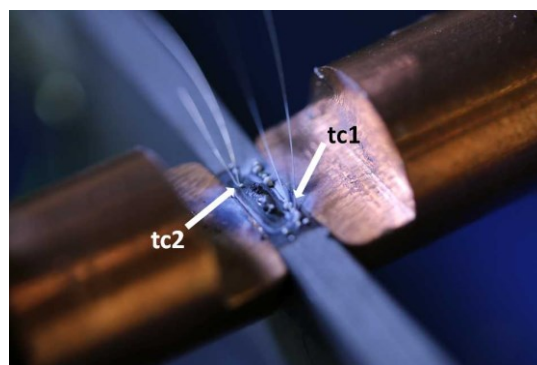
assemblage symétrique après soudage avec visualisation des deux thermocouples.
